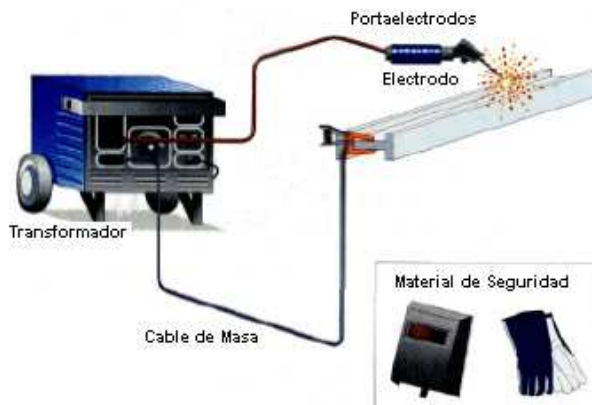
Equipo para la soldadura SMAW
